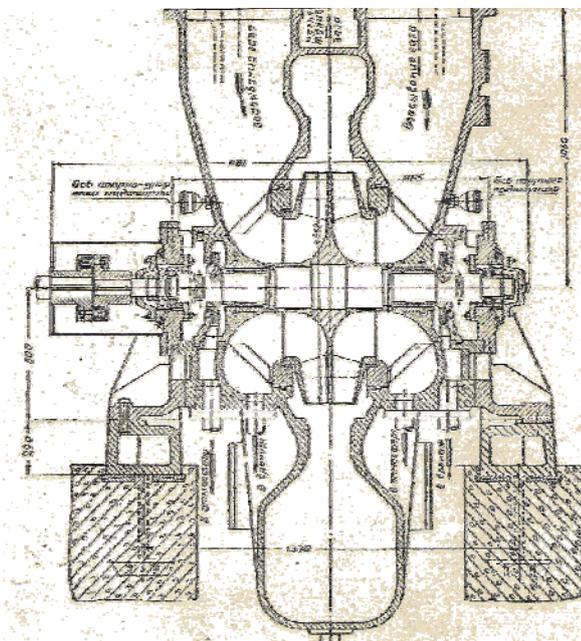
а. Типичный центробежный компрессор с небольшим повышением давления. Может применяться как тягодутьевой компрессор (при больших размерах корпус сварной), в производстве цемента и пр.
